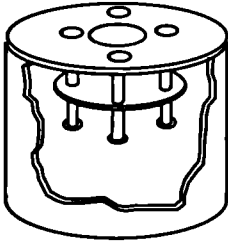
Схема конструкции поршневого цилиндра для гидравлоса
